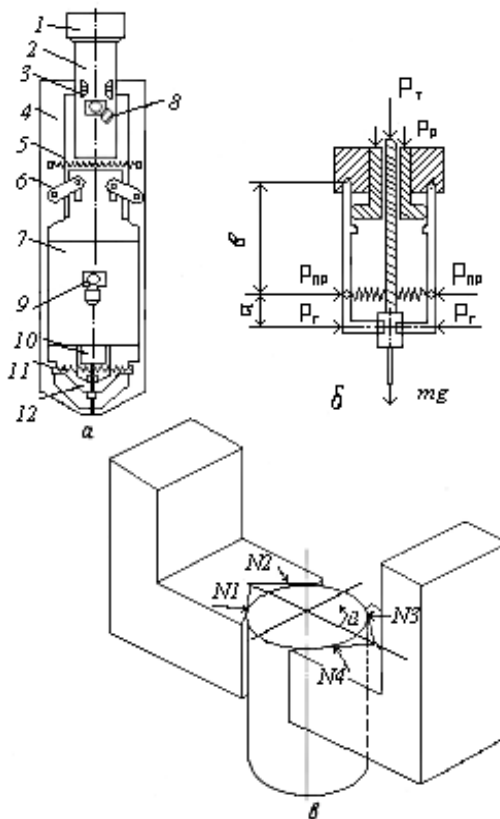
Устройство захвата конденсаторов: а – общий вид; б – расчетная схема
